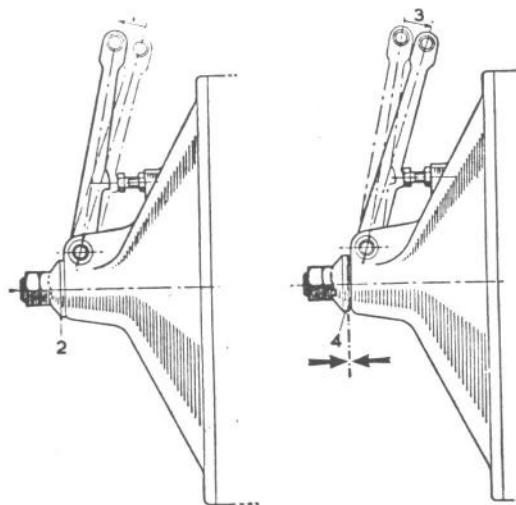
Posiciones de la palanca de mando del mecanismo de embrague y reglaje del tope.
